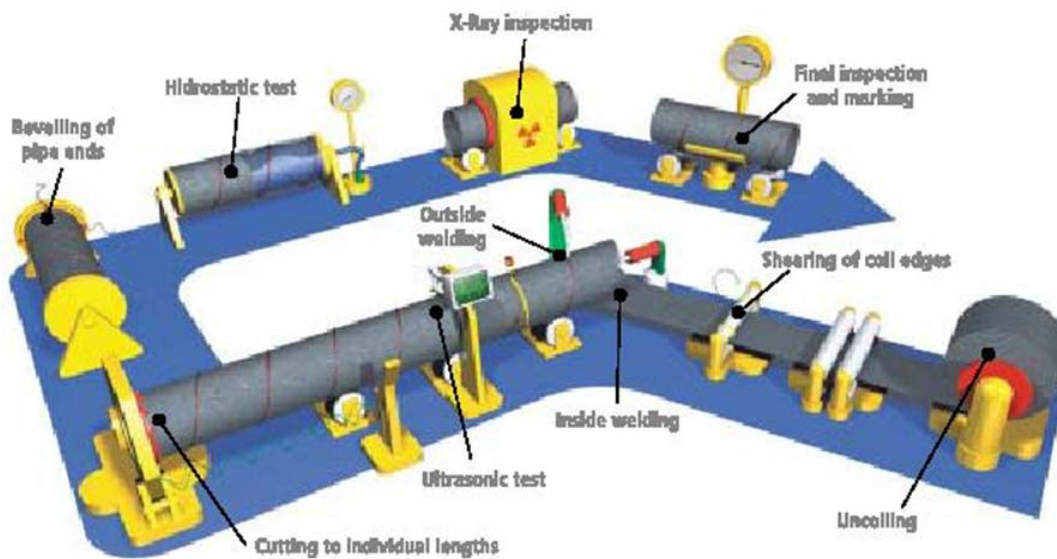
Procédé de fabrication des tubes soudés en spirales [2].
